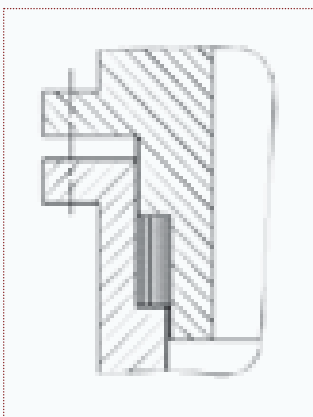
Неподвижное РГС с цилиндрической навитой прокладкой
